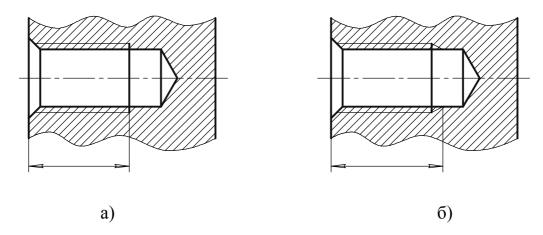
Способы указания размера длины резьбы в отверстии
